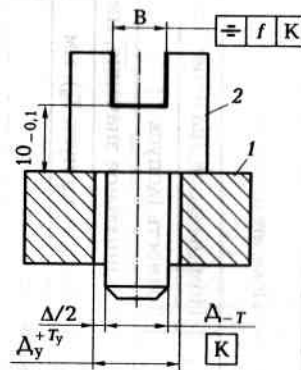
Схема установки заготовки при фрезеровании паза
